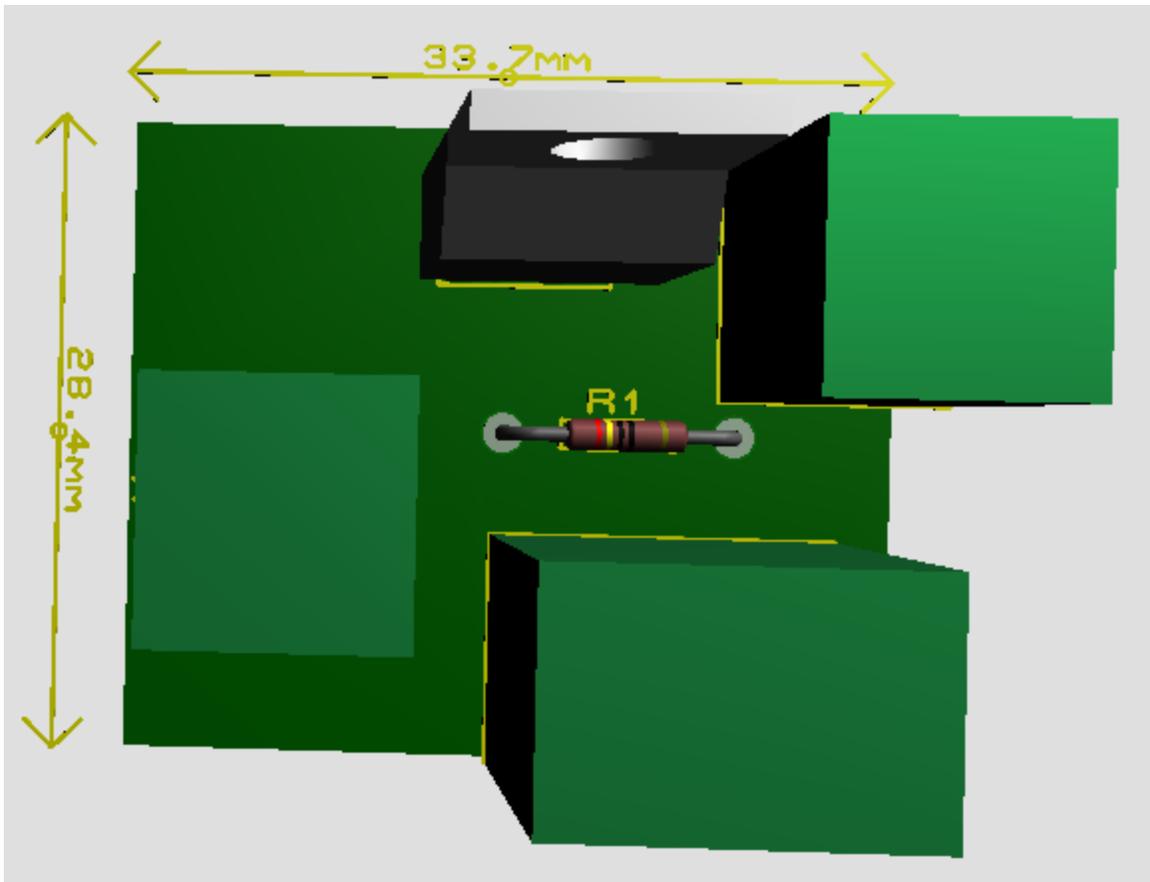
Diseño final hecho en PCB layout de proteus
